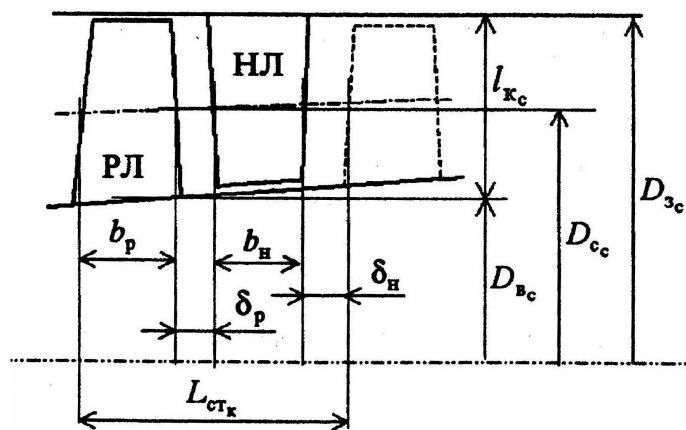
Ескіз проточної частини середнього розрахункового ступеня осьового компресора
